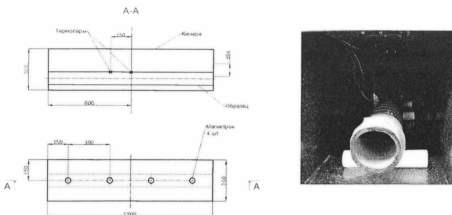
Схема размещения заготовки детали внутри камеры СВЧ-нагрева
